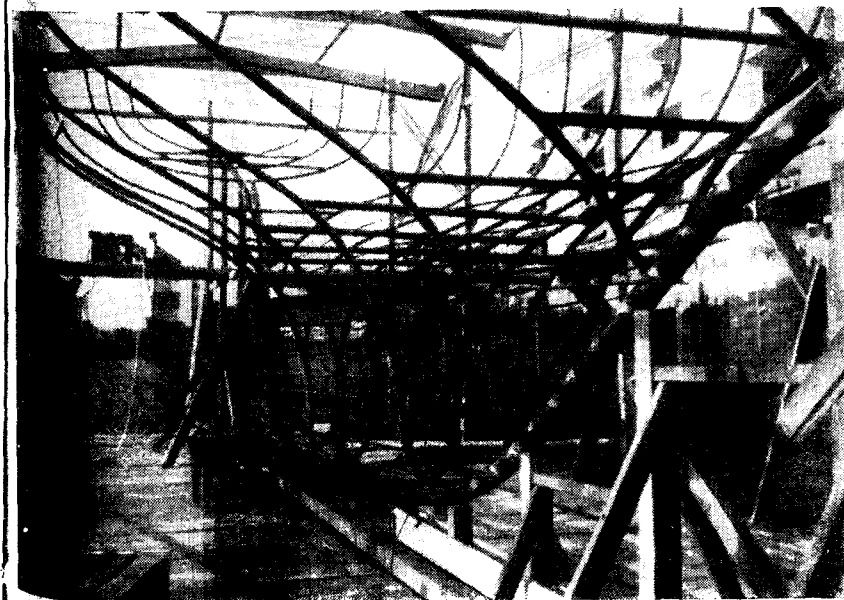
Каркас армоцементной яхты на стапеле. Установлены шпангоуты и укреплены продольные арматурные стержни. Хорошо видна мощная труба, составляющая основу килевого профиля.
